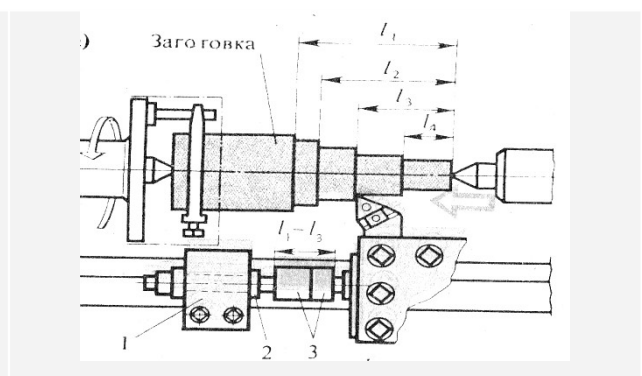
Обтачивание ступенчатого вала по упору с длиноограничителями: 1 – упор; 2 – регулировочный винт; 3 – мерные плитки - длиноограничители
